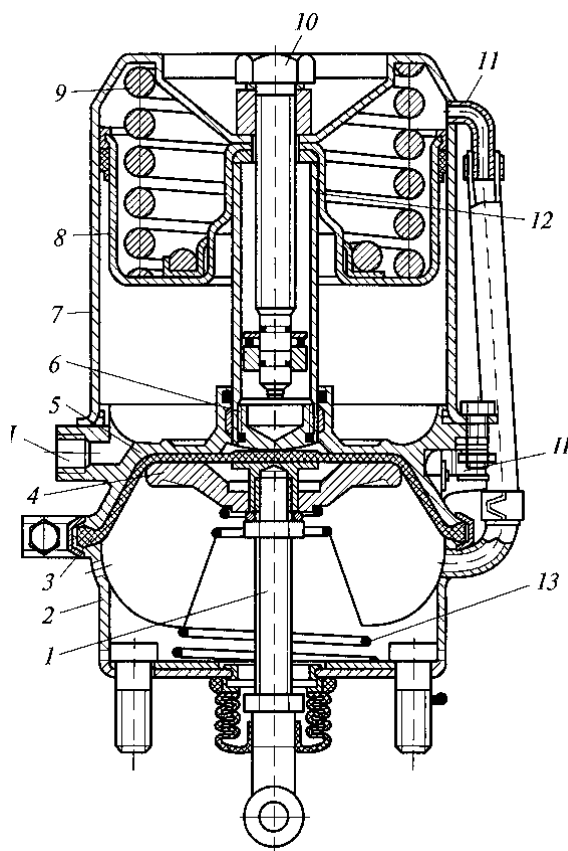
Гальмівна камера з енергоакумулятором: 1 - шток; 2 - корпус; 3 - діафрагма; 4 - диск; 5 - фланець; 6 - підп'ятник; 7 - циліндр; 8 - поршень; 9, 13 - пружини; 10 - гвинт; 11 - трубка; 12 - штовхач; I, II - виводи
